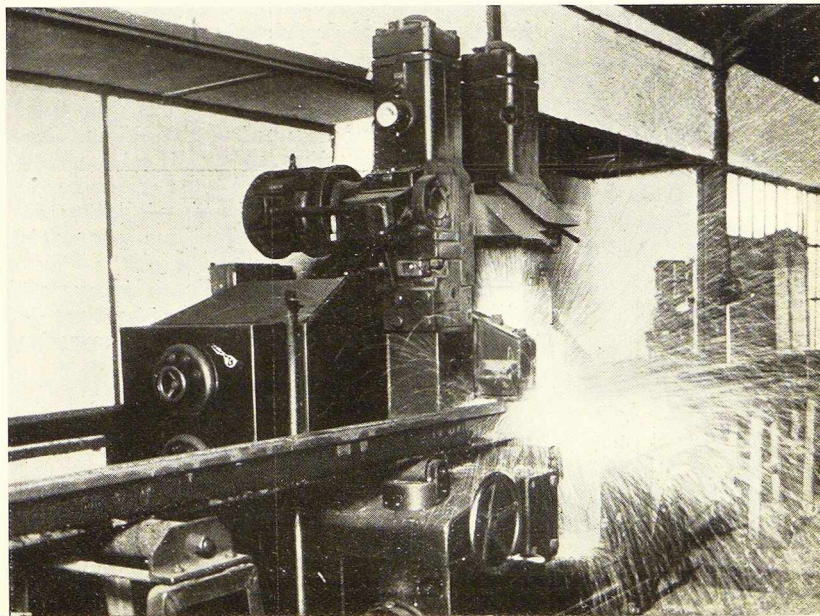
Profilage du rail à l'endroit de la soudure.
